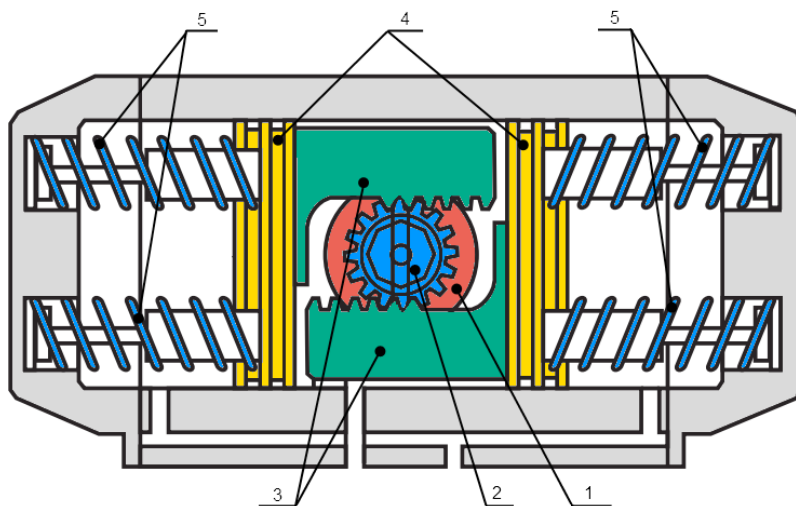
Конструкция пневмопривода с механизмом шестерня-рейка
